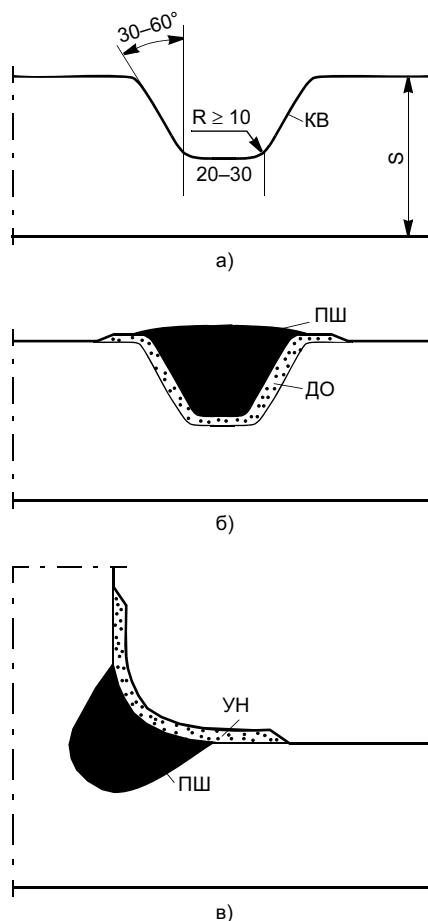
Рекомендуемая форма выборки (а) и ремонтных заварок для стыкового (б) и углового (в) швов при ремонте литых корпусных деталей трубопроводов I категории (КВ — контур выборки; ДО — двухслойная облицовка)
